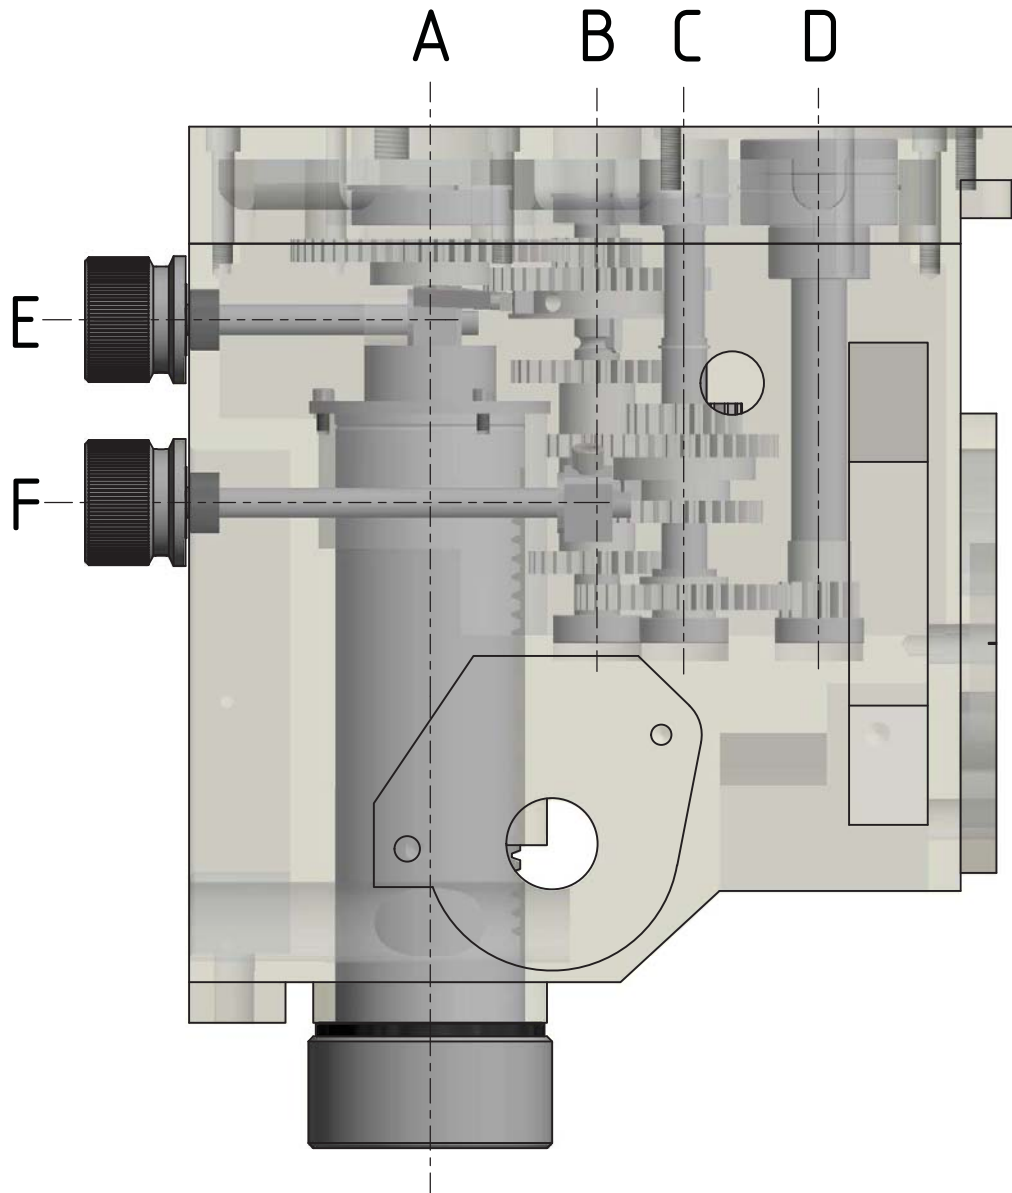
Fräskopf 1 von 6 - Milling head 1 von 6
